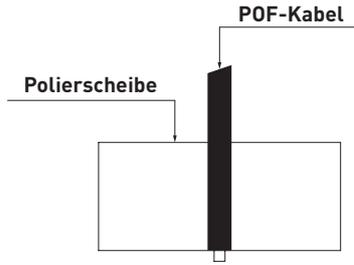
Polierscheibe mit Führung für die POF-Faser
